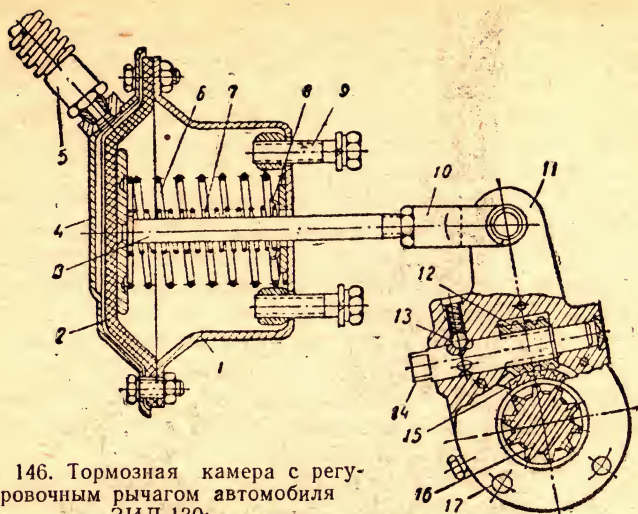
Тормозная камера с регулировочным рычагом автомобиля ЗИЛ-130:
